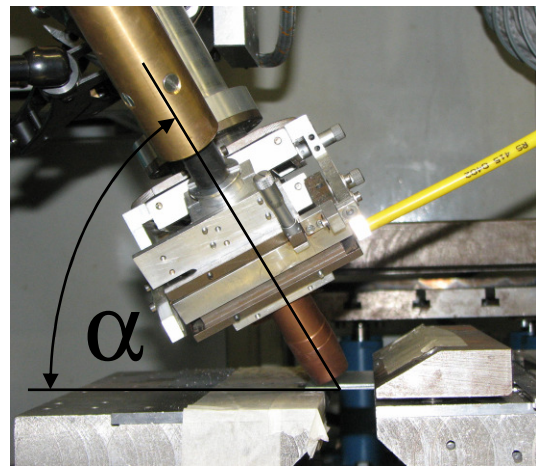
Ansicht des Versuchsaufbaus in Schweißrichtung
